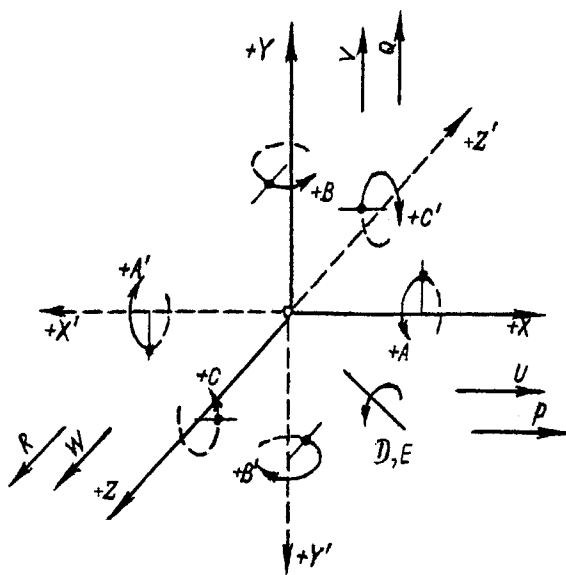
Стандартна система координат верстатів з ЧПК
